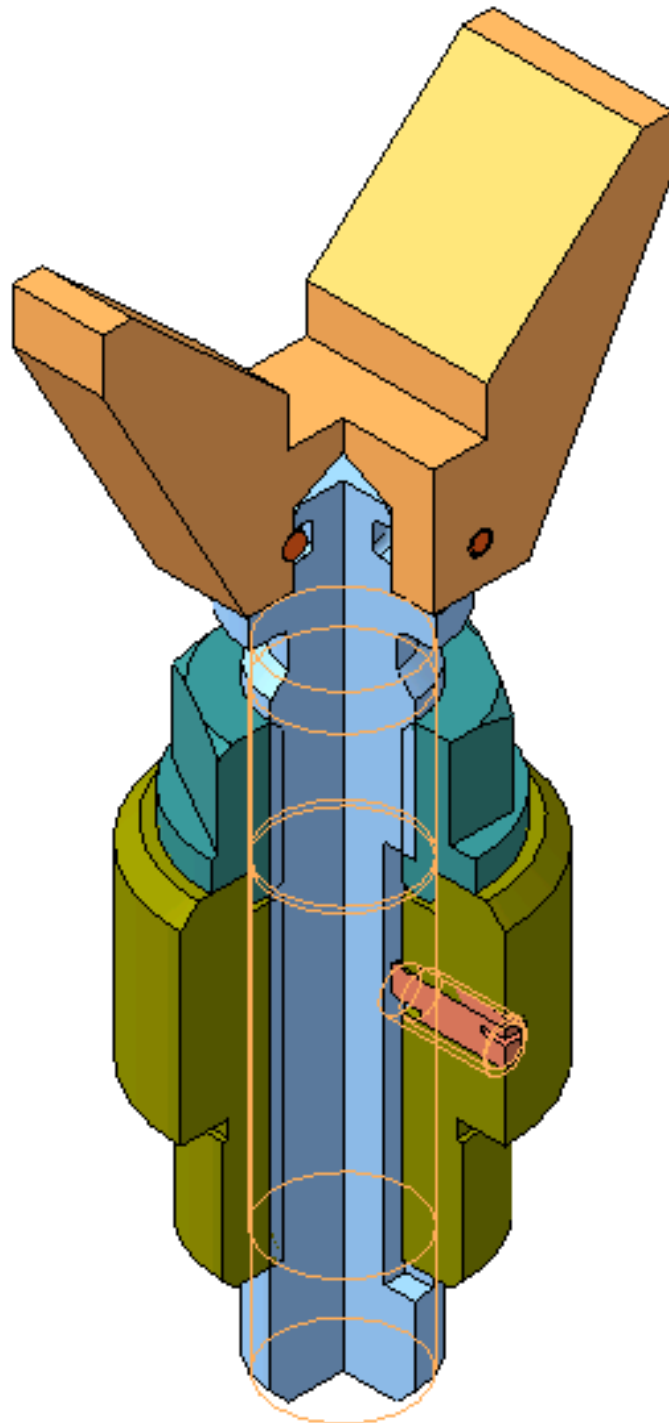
3D-модель сборки изделия «Подпорка винтовая встроенная»
